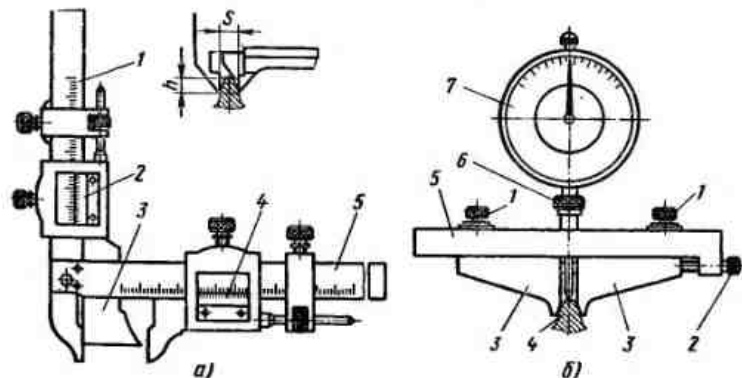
Штангензубомер (а) и тангенциальный зубомер (б)
